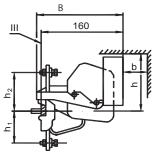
Габаритные и установочные размеры двух- и трехполюсных контакторов типа КТП 6000 на ток 100 А; 160 А.
